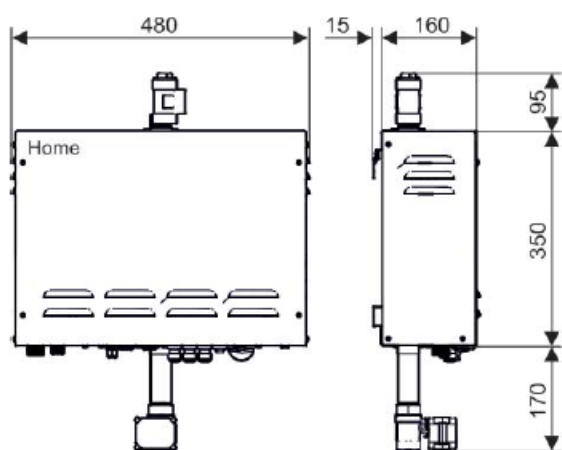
Tylö Generatore di vapore Tipo HOME, dimensioni in millimetri
